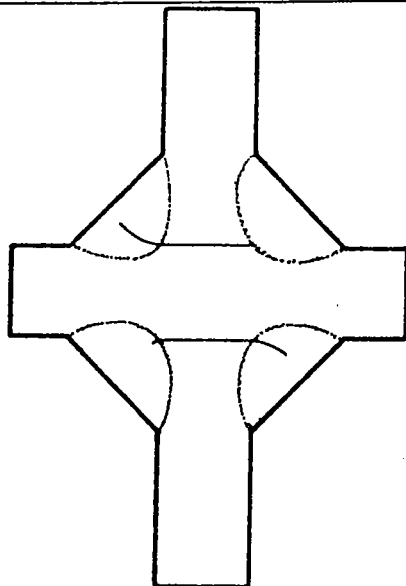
Type de fissuration dans le joint soudé utilisé par FORD
